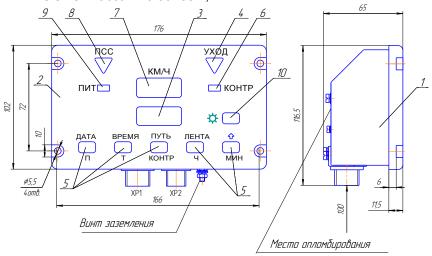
Габаритные и установочные размеры БИ-4ДВ
